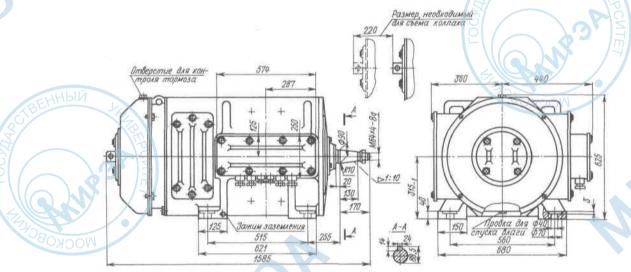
Габаритные, установочные, присоединительные размеры двигателя ДПМ 62 с тормозом
